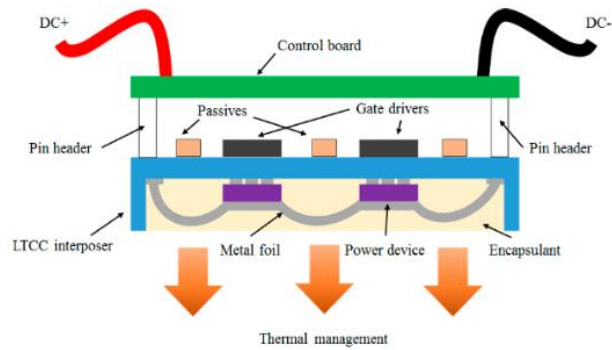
Integrated wire bondless power module, IWPM* [19]
